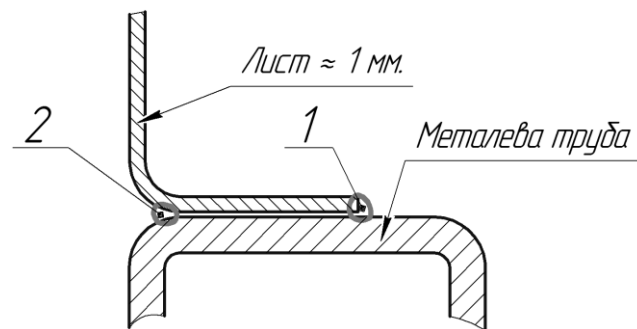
Переріз з'єднання рамно-оболонкової конструкції
